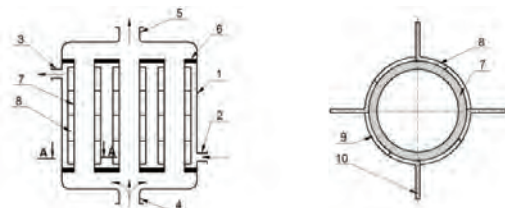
Схема кожухотрубного теплообменника с гильзой, установленной на каждой наружной поверхности трубки и с ребрами, выполненными из боковой поверхности гильзы и отогнутыми наружу:
